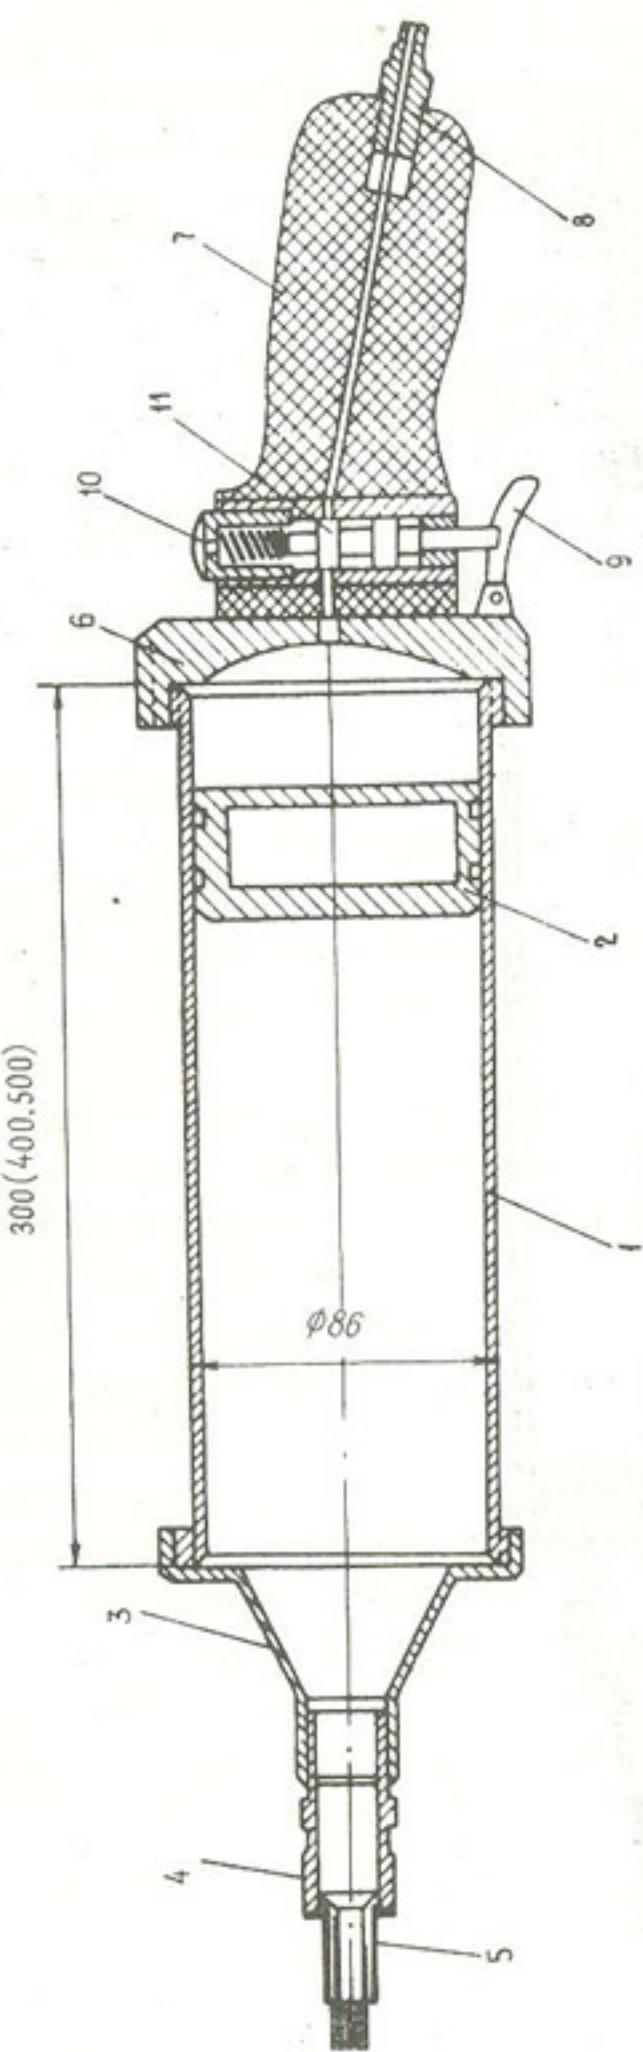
Пневматический шприц для нанесения тиоколовых мастик: I-цилиндр;
